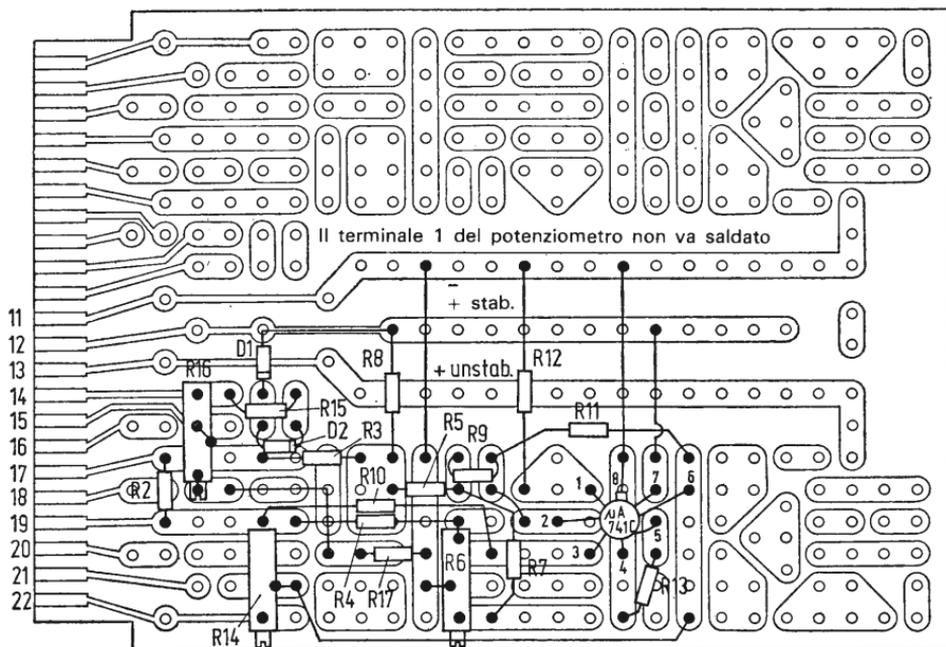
Disposizione dei componenti del circuito di fig. 18 (senza la parte alimentazione), visti dal lato isolante del circuito stampato
